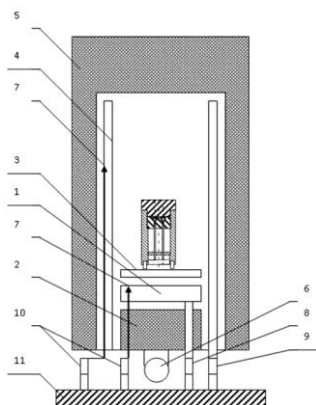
Нагревательные элементы установки ГИП: 1 - нижний нагревательный элемент; 2 - теплоизоляция нижнего нагревателя; 3 - рабочий стол; 4 - боковой нагревательный элемент; 5 - теплоизолирующий кожух; 6 - устройство быстрого охлаждения; 7 - термопары рабочие; 8 - токоввод нижнего нагревательного элемента; 9 - токоввод бокового нагревательного элемента; 10 - термопарные разъемы; 11 - фрагмент нижней крышки СВД.
